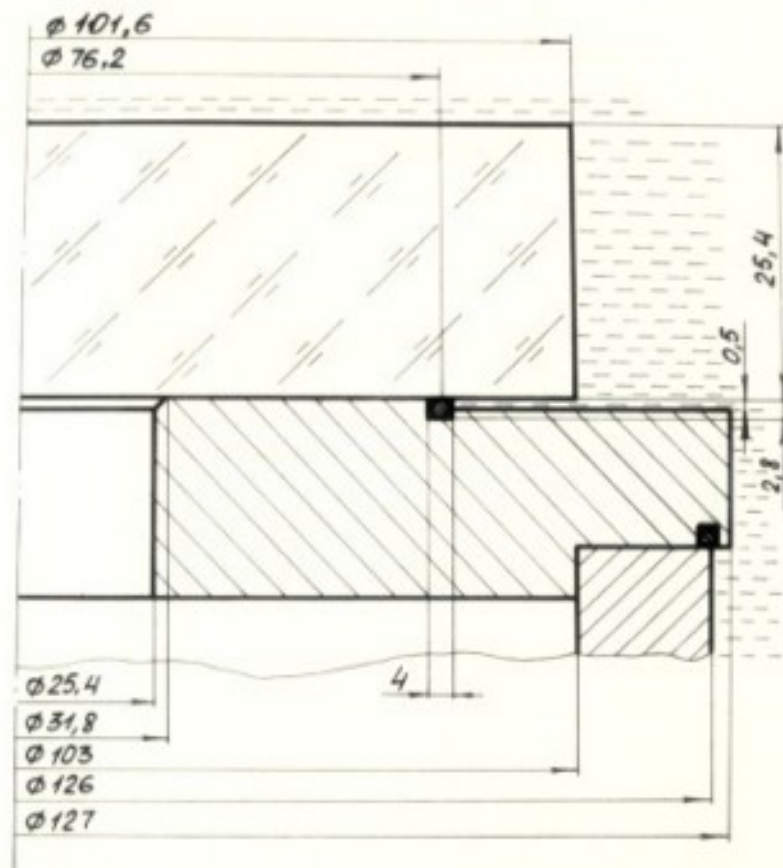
Глубоководный иллюминатор конструкции Х.Е.Эджертона и Л.Д. Хоудли
